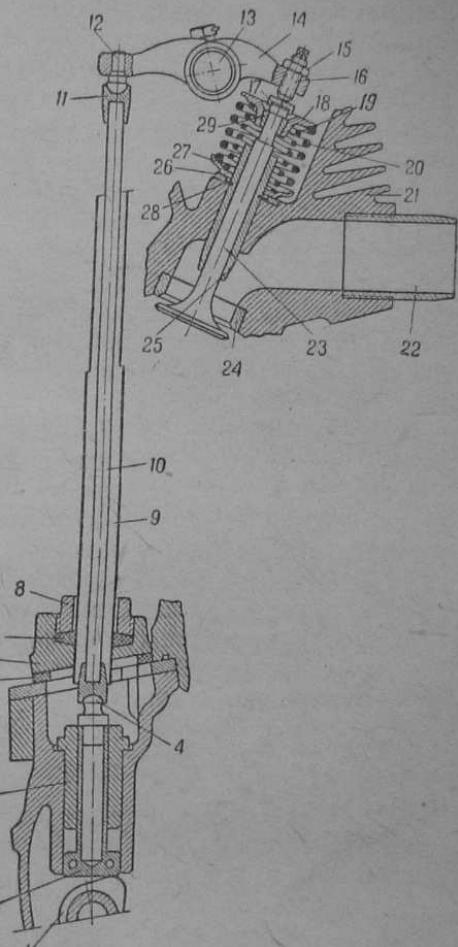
Конструктивная схема верхнеклапанного газораспределения двигателя М-76:
